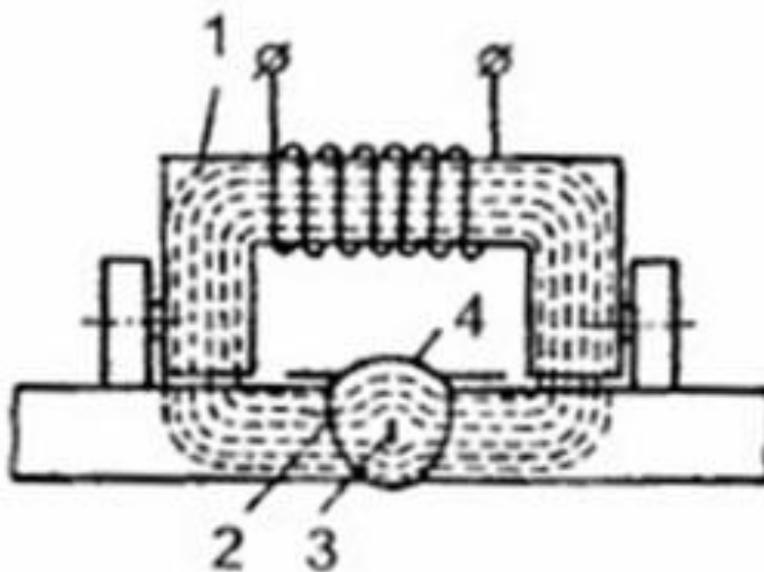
Проверка качества сварных швов магнитной дефектоскопией
